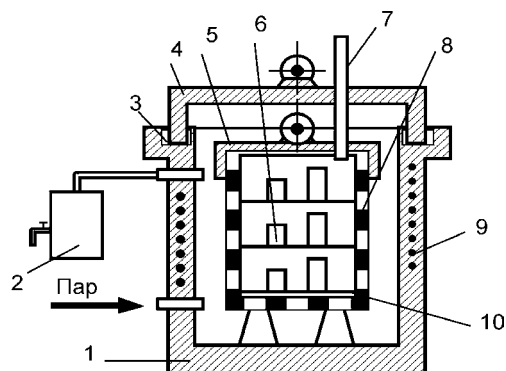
Схема установки для обработки деталей в атмосфере пара:
